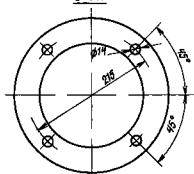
21 Габаритные и установочные размеры фазорегуляторов типа ФР4
